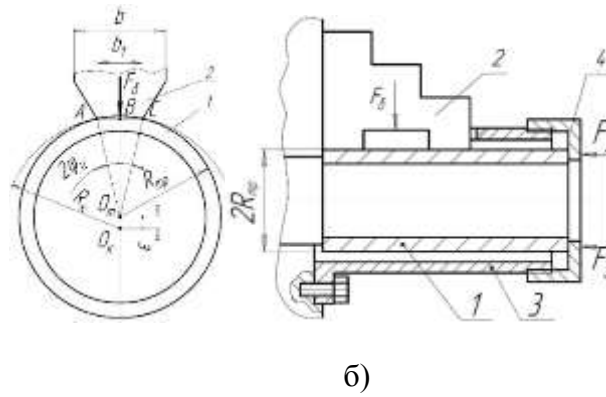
Розрахункова схема для визначення радіуса кулачка R_k , який створюється розточкою (а) та схема закріплення заготовки в патроні (б): 1 – оброблювана заготовка; 2 – кулачок 3 – труба; 4 – затискна гайка.
